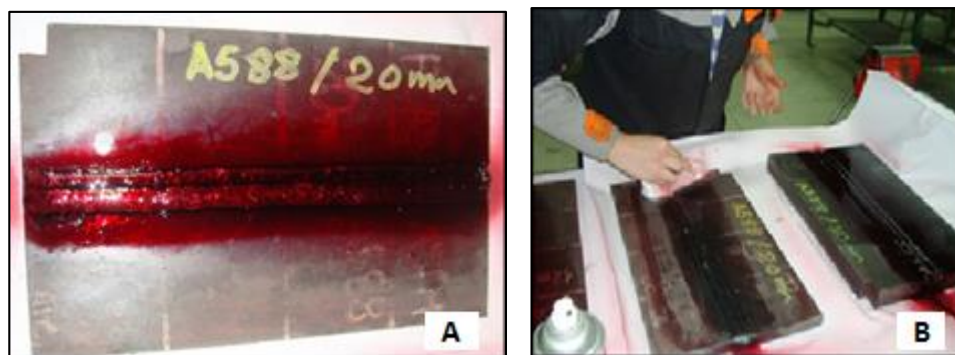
Limpieza de cupones de soldadura.
